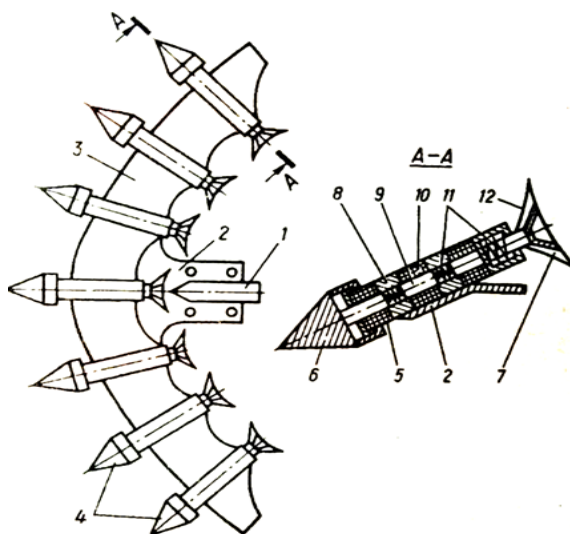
Вибромагнитный почвообрабатывающий рабочий орган
